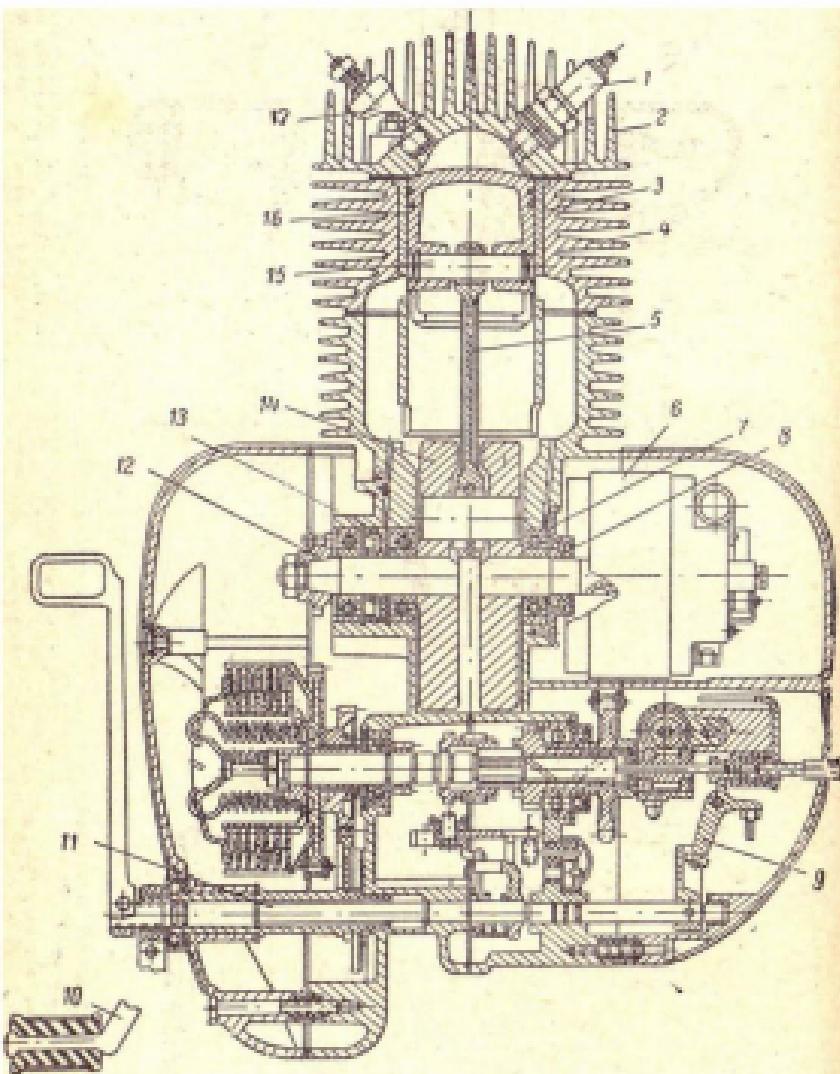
Блок двигателя с коробкой передач мотоцикла К-175:
